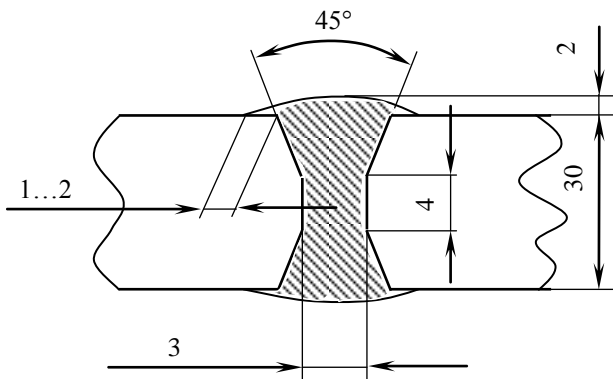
X-образная подготовка кромок стыкового соединения и некоторые размеры сварного шва
